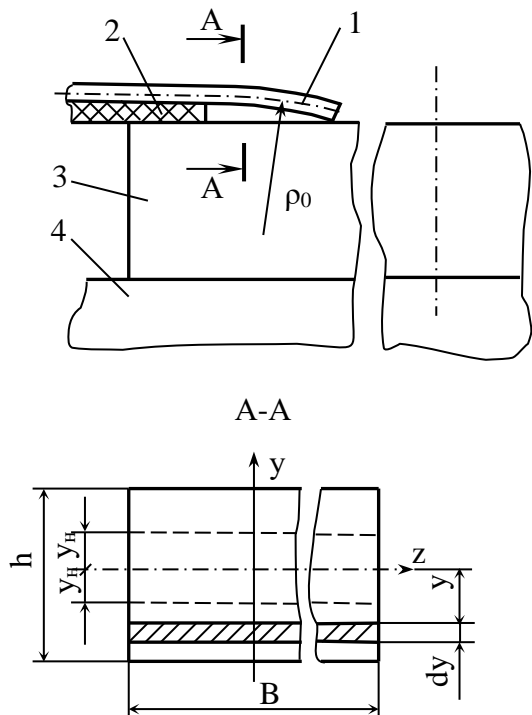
Схема упругопластического изгиба паучкового вывода при ультразвуковой сварке: 1 – вывод; 2 – пленка полиимида; 3 – кристалл; 4 – подложка
